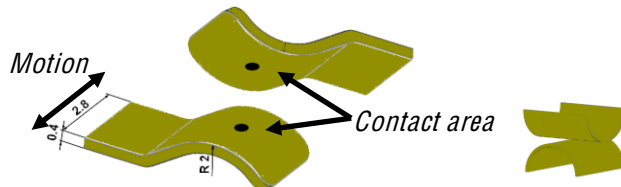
Kontaktfedern mit punktförmiger Kontaktzone
